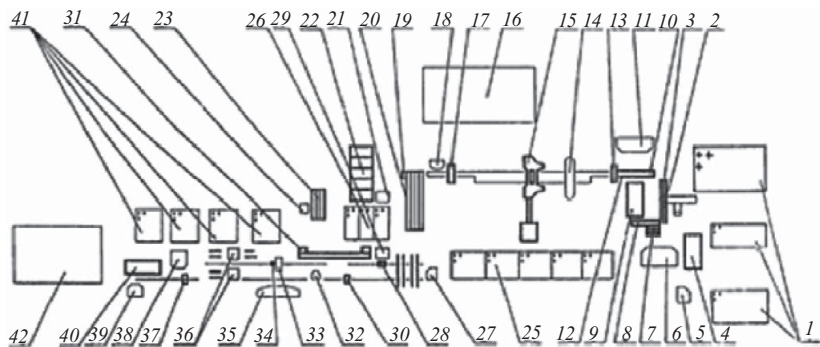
Схема расположения основного технологического оборудования стана 850: 1 – склад блюмов ЭСПЦ-2, 2 – приемный ролик, 3 – загрузочная решетка с термостатом, 4 – подогревательная печь, 5 – ПУ-1а, 6 – ПУ-1, 7 – загрузочно-разгрузочное устройство, 8 – загрузочный ролик печи, 9 – нагревательная печь, 10 – ролик возврата, 11 – ПУ-2, 12 – ролик выдачи, 13 – гидросбив, 14 – ПУ-3, 15 – реверсивная клеть, 16 – участок ремонта технологического оборудования, 17 – пила горячей резки, 18 – ПУ-4, 19 – маркировочная машина, 20 – холодильник, 21 – ПУ-5, 22 – колодцы замедленного охлаждения, 23 – передаточный транспортер, 24 – ПУ-6, 25 – промежуточный склад, 26 – промежуточный склад 2, 27 – ПУ-8, 28 – правильная машина, 29 – ПУ-9, 30 – дробеструйная установка, 31 – установка магнитной дефектоскопии, 32 – ПУ-10, 33 – ПУ-11, 34 – установка ультразвукового контроля внутренних дефектов, 35 – ПУ-7, 36 – зачистные станки ПУ-12 и ПУ-13, 37 – пила холодной резки, 38 – ПУ-14, 39 – ПУ-15, 40 – вязальные машины, 41 – склад квадратных заготовок, 42 – склад готовой продукции
